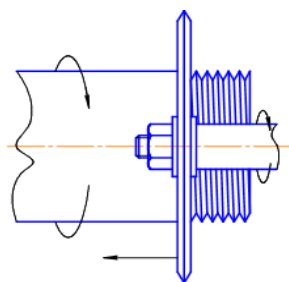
Схема шлифования наружной резьбы однопрофильным шлифовальным кругом
